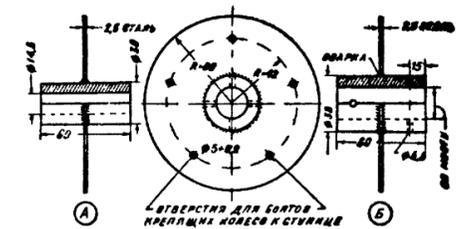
Ступицы переднего (А) и заднего (Б) колеса. Втулки изготавливаются из стали 40. Диски — из стали 20. Перед сваркой все четыре диска зажимаются вместе, и в них сверлят отверстия Ø 5,3 для болтов, крепящих колеса к ступице
